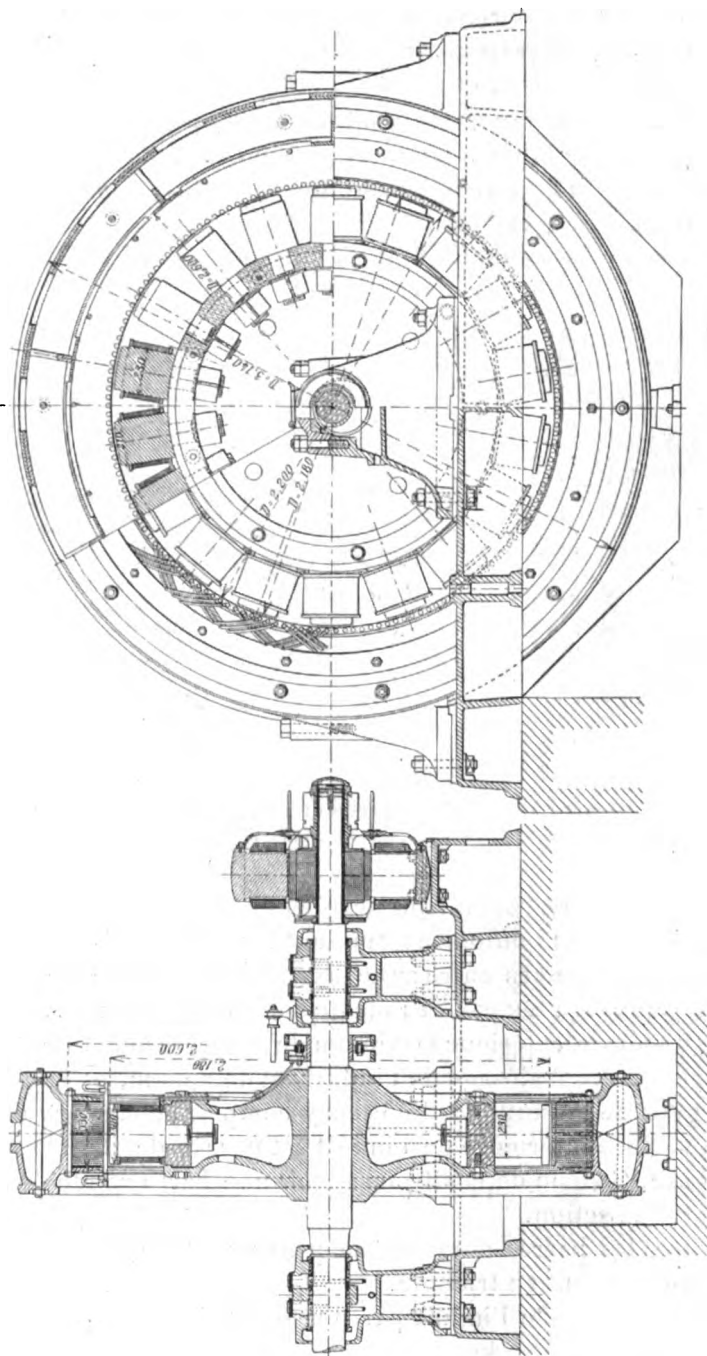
et 3. — Vues d'ensemble et coupes de l'alternateur de 400 kilovolts-ampères de MM. J.-J. Rieter et C^{ie}.
